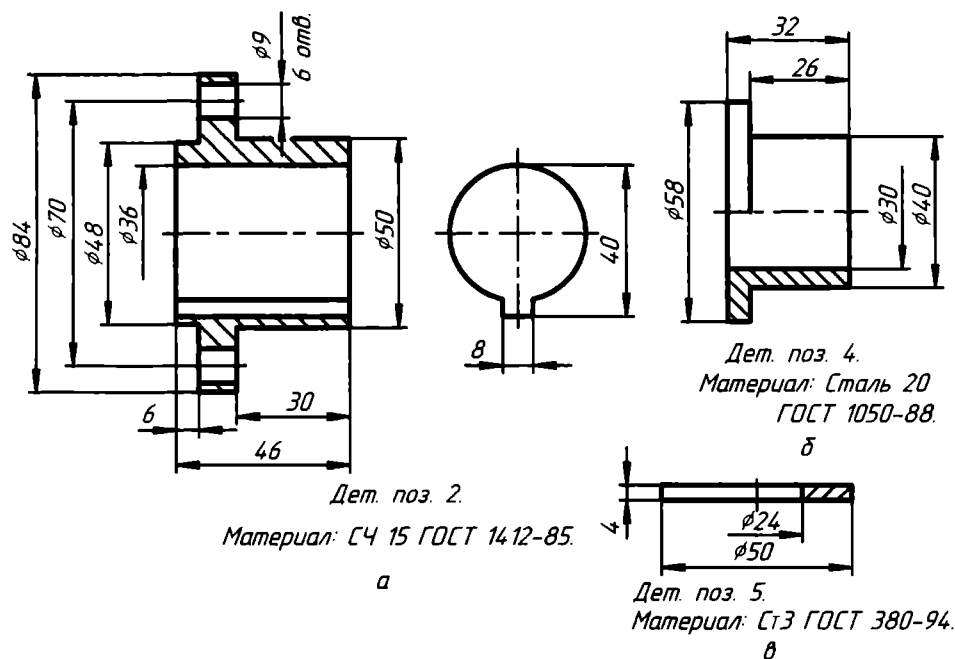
Чертежи: а — крышки; б — втулки; в — шайбы
